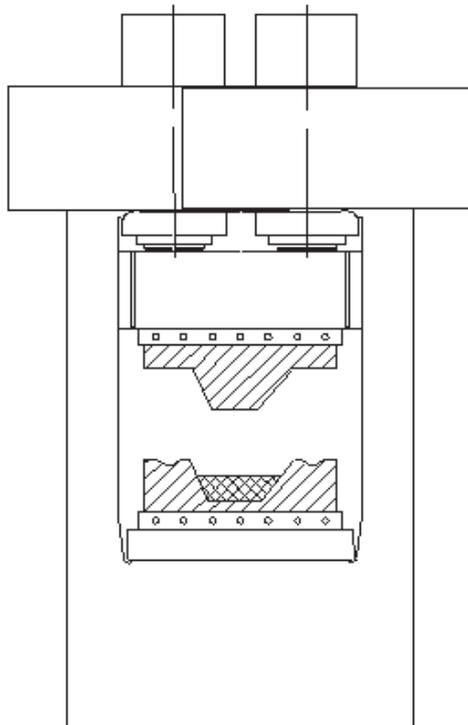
Presse zum Formpressen mit geöffnetem Werkzeug und mit Formmasse beschickt
